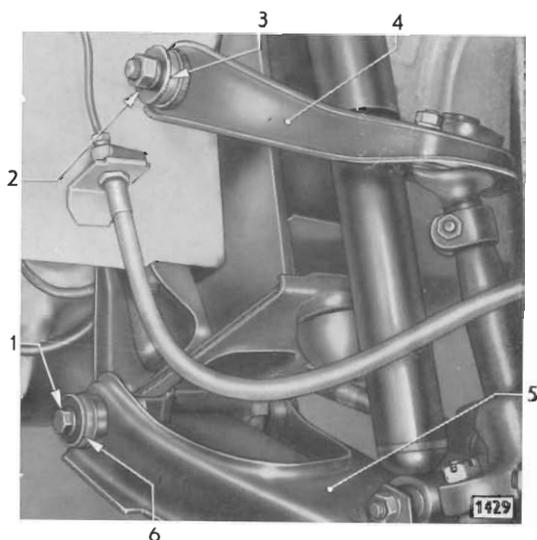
Sechskantmutter am oberen Lenker und Sechskantschraube am unteren Lenker lösen
